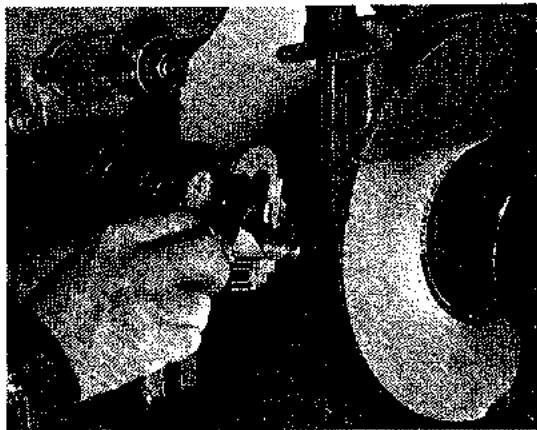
Calibre de horquilla con indicador, tipo fijo (Federal Products Corp.)
